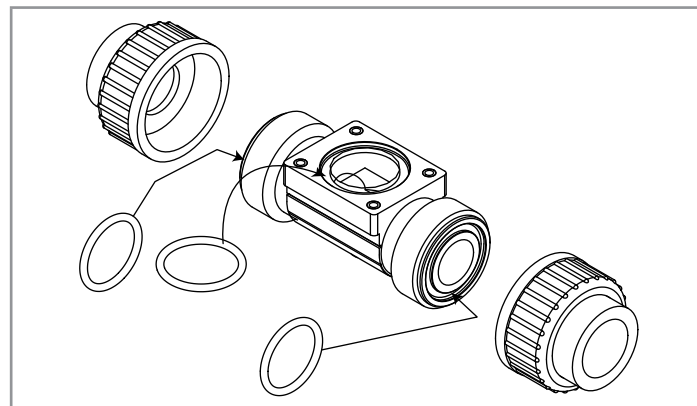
O-Ring-Dichtungen für Kunststoff-Fitting
